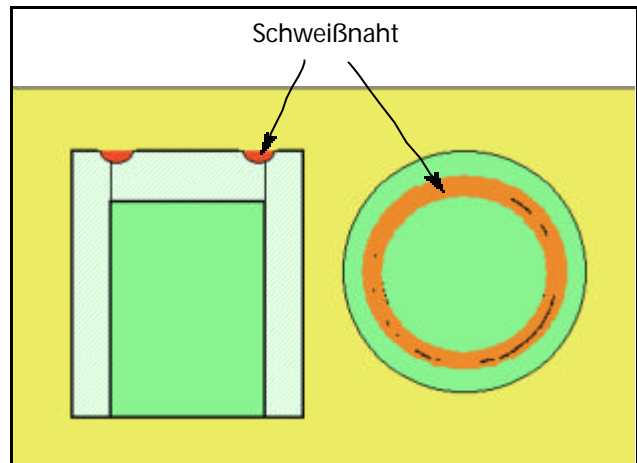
Rohr mit eingeschweisster Deckplatte
